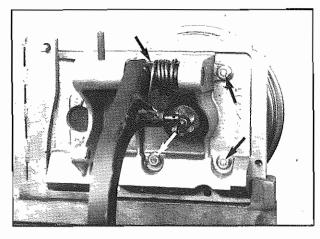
Dadi fissaggio pompa servofreno Brake booster nuts
